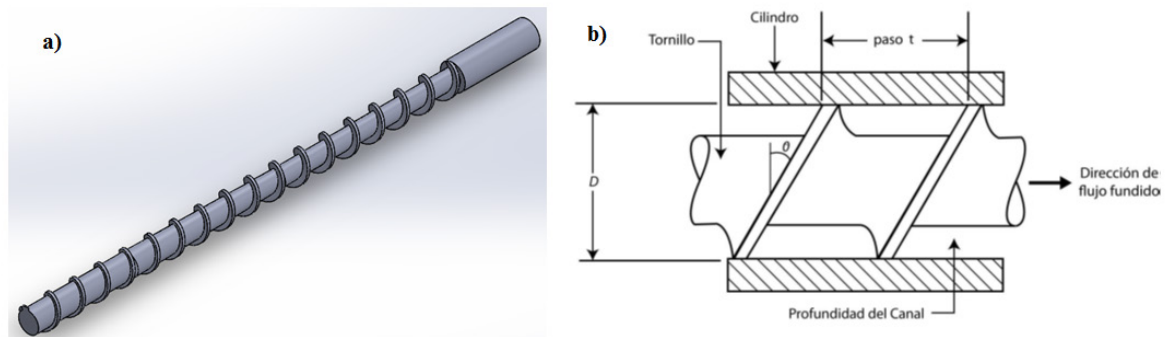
a) Diseño geométrico del husillo y b) Partes del husillo
